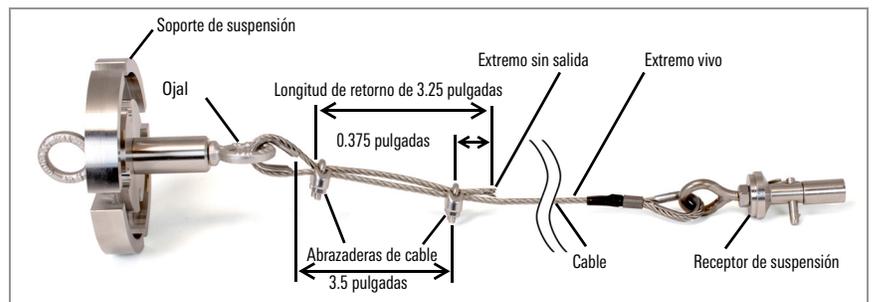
Cable de suspensión ensamblado (ejemplo)
